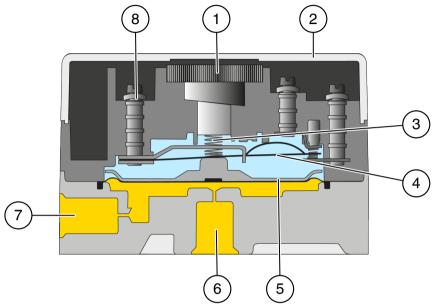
Funktionszeichnung Druckwächter mit einer Druckkammer
